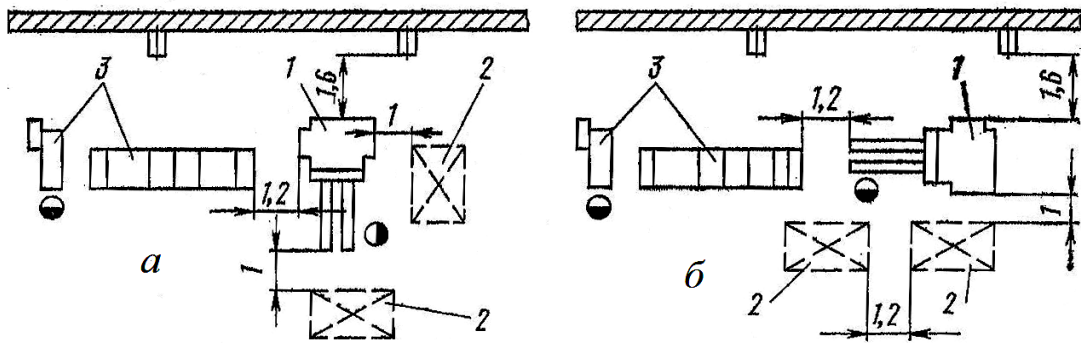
Схеми розташування гибочно-штампувальних горизонтальних кривошипних пресів (бульдозерів):
